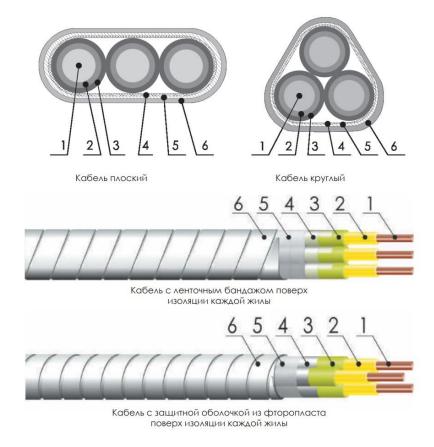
Схематичные чертежи поперечного сечения кабелей и внешний вид конструктивных элементов:
